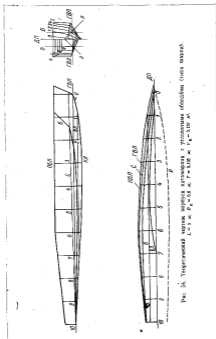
Теоретический чертеж корпуса катамарана с округлыми шпангоутами (план шпангоут).
